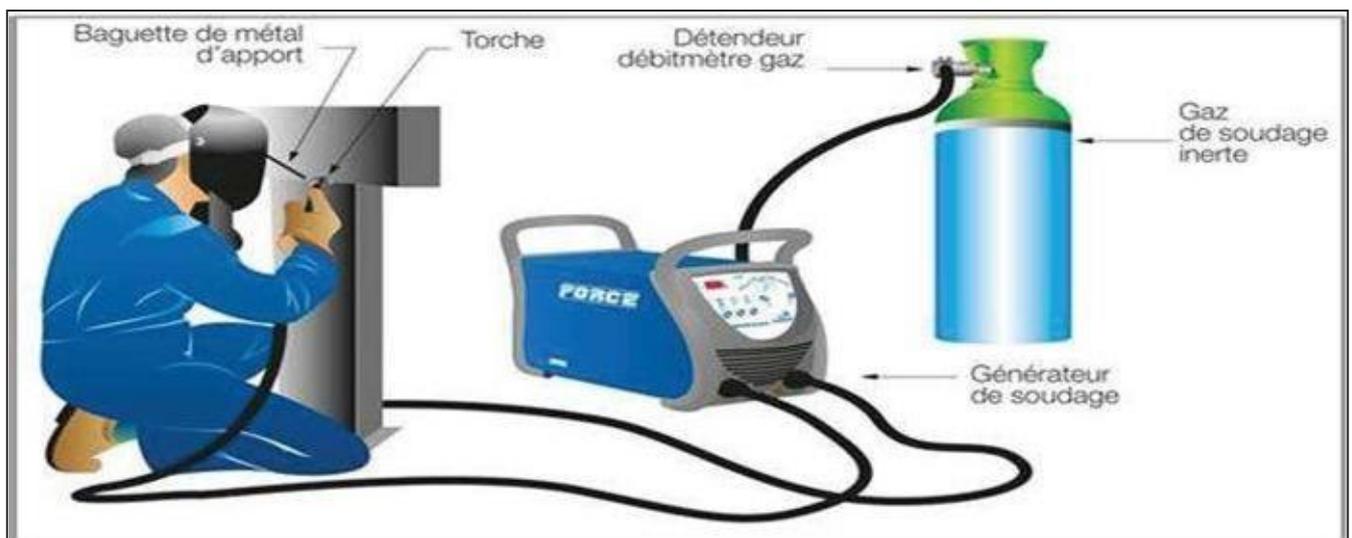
Installation manuelle pour soudage TIG [2]
